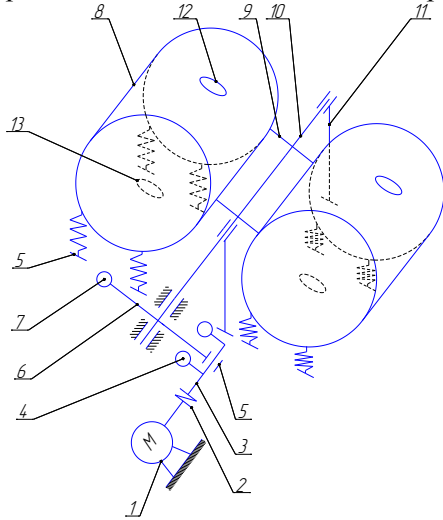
Принципова схема вібраційного млина кутових коливань: 1 – електродвигун; 2 – еластична муфта; 3 – приводний вал; 4 – дебаланси; 5 – підшипниковий вузол; 6 – штанга; 7 – противага; 8 – підпружинені помольні камери; 9 – траверси; 10 – вісь; 11 – стійки; 12, 13 – патрубки відповідно для подачі та розвантаження технологічного середовища.
